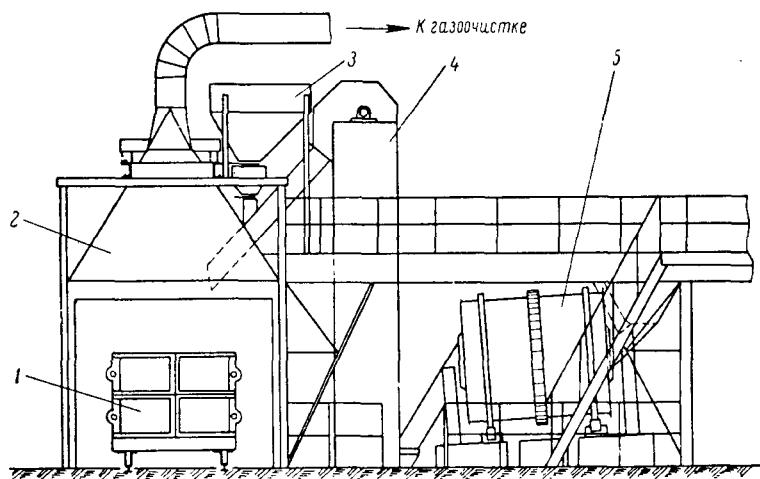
Установка для внепечной выплавки металлического хрома на блок:
